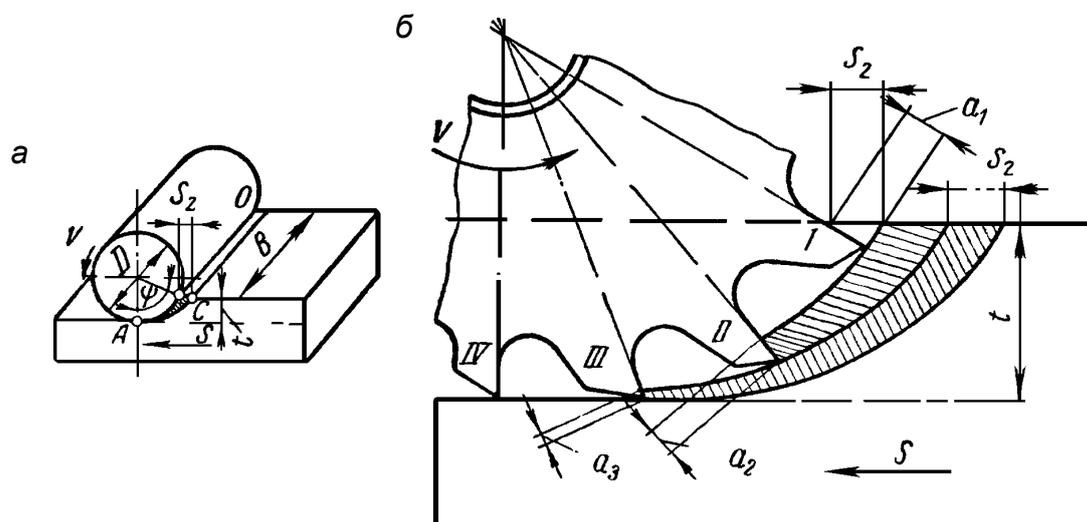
Схема работы цилиндрической фрезы с прямыми зубьями: а – перемещение инструмента при фрезеровании; б – процесс обработки фрезой
